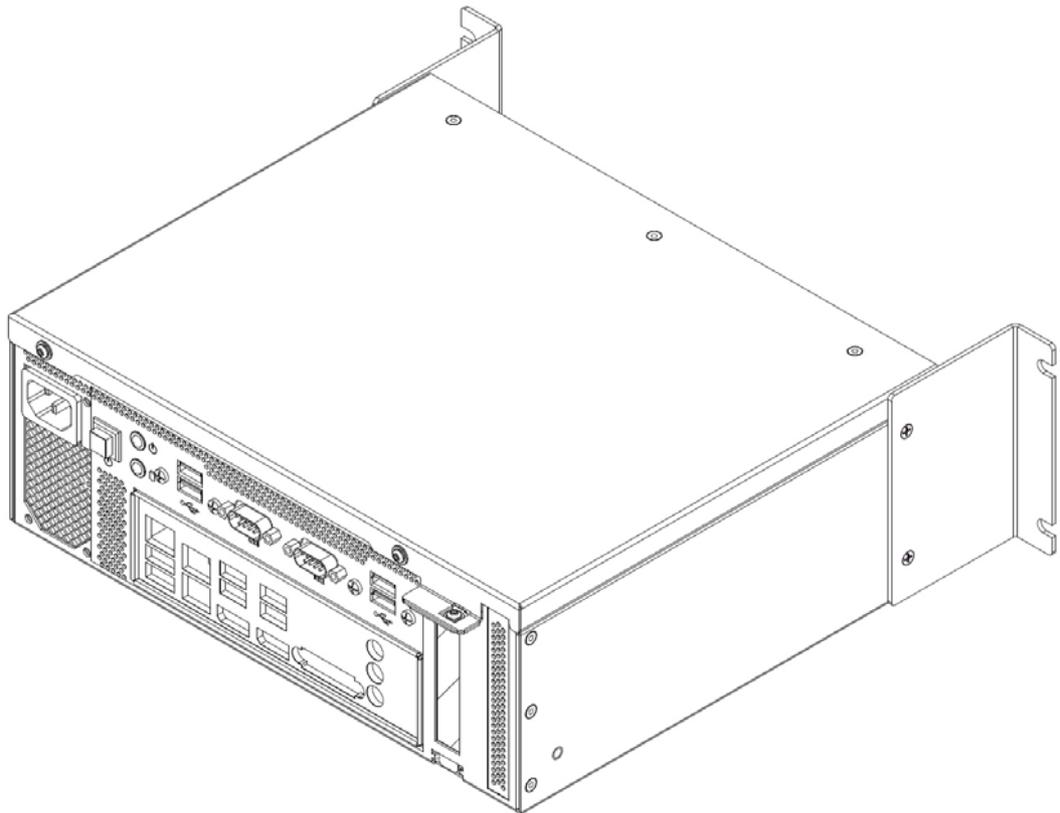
KBox B-101 mit montierten Halterungen für Wandmontage
